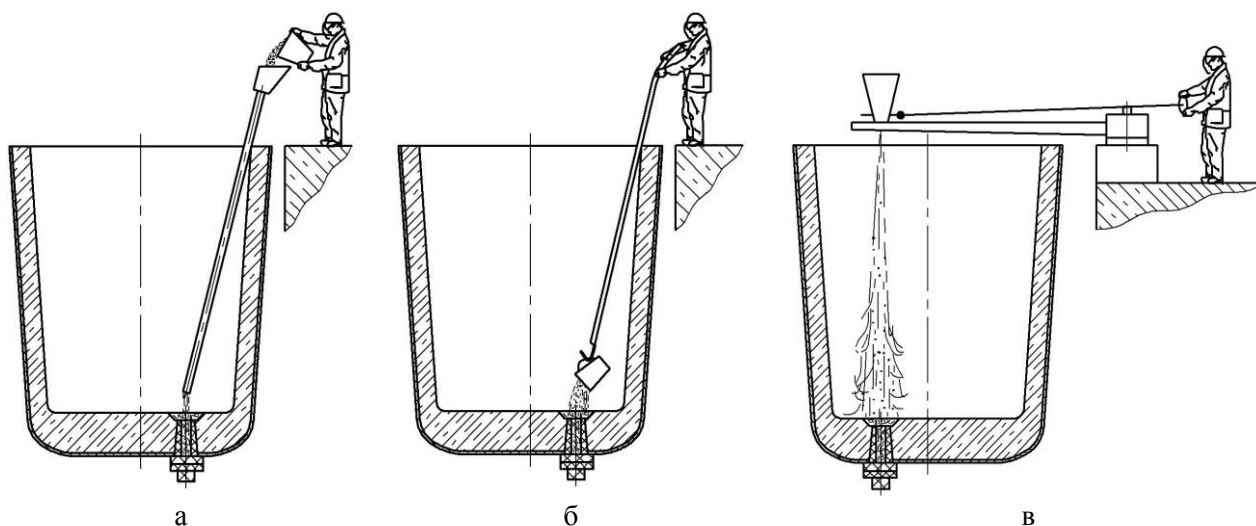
Способы подачи стартовой смеси в канал сталеразливочного ковша:
